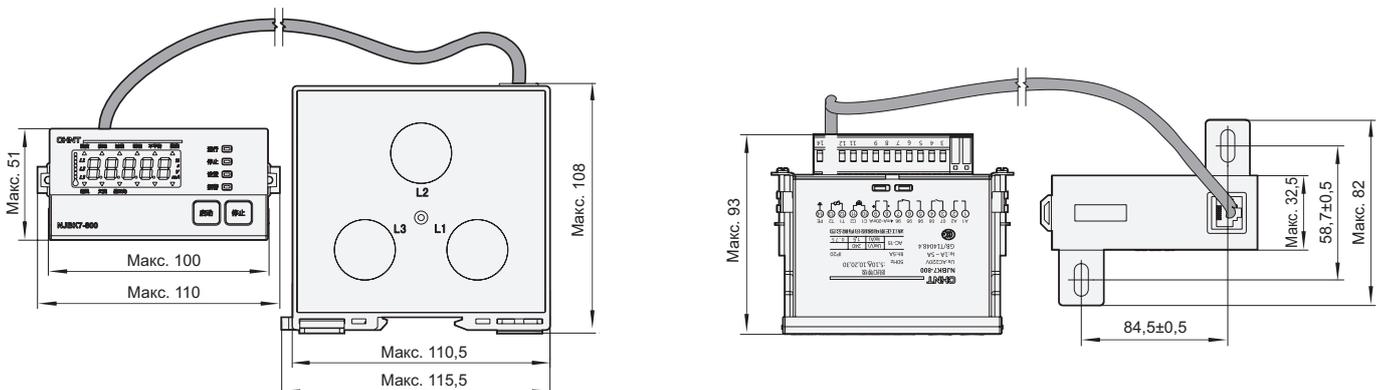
Габаритные и установочные размеры устройства защиты с номинальным током 100 А
